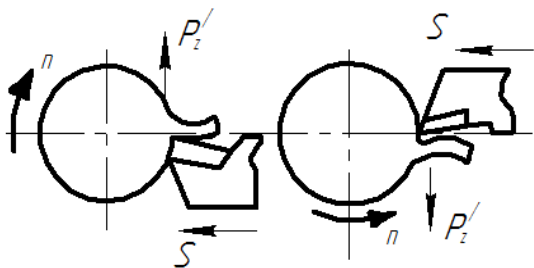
Відрізування заготовок при прямому (а) і зворотному (б) обертанні шпинделя
